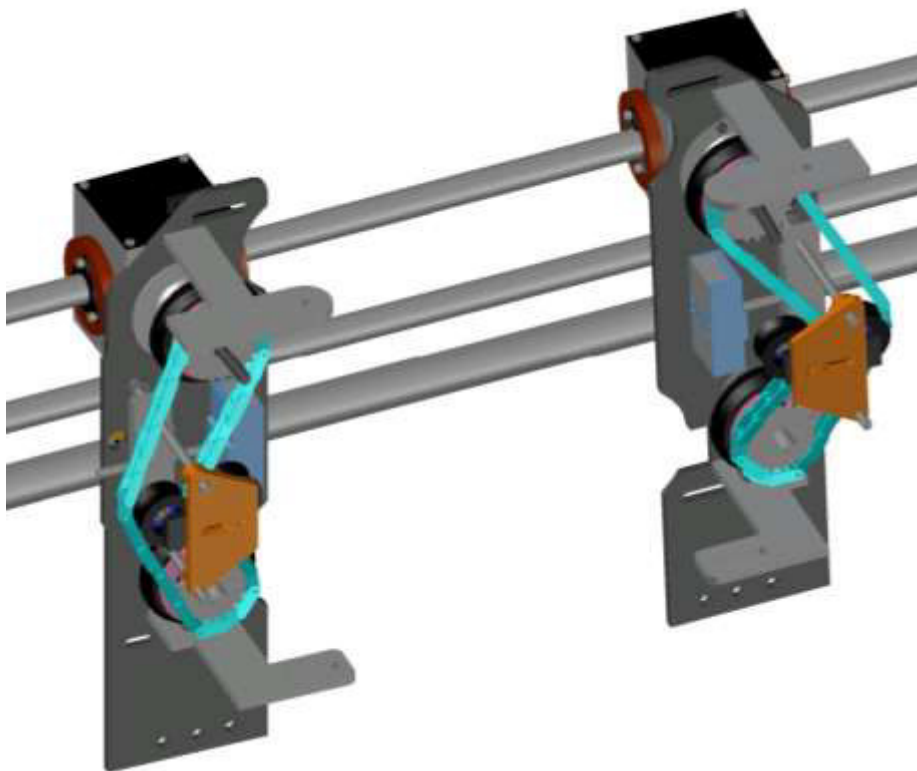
Templador de cadena montado sobre placas de soporte.
